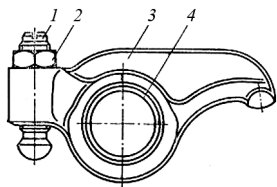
Коромысло ГРМ в сборе: 1 – регулировочный винт; 2 – контргайка; 3 – коромысло; 4 – втулка
